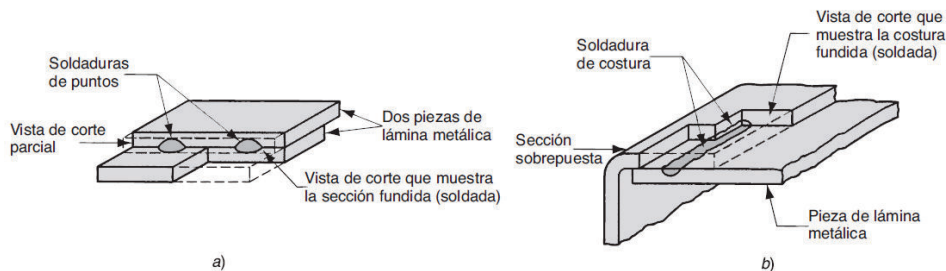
(a) Soldadura de puntos y (b) Soldadura de costura.
